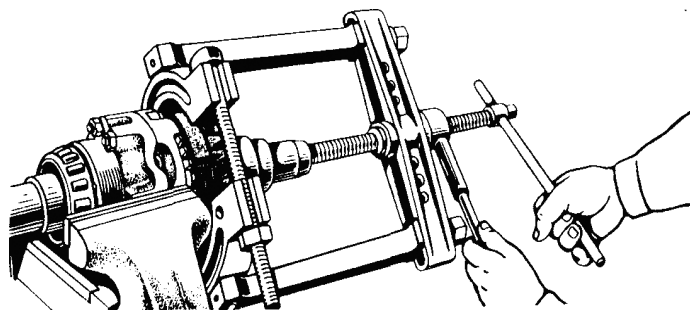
Спрессовка ведомой шестерни главной передачи.
